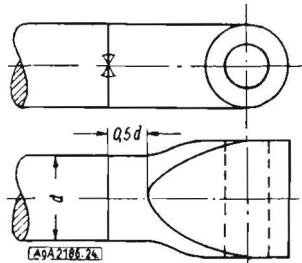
Ähnliche Ausführung wie in Bild 23, doch ist hier das Gelenkauge aus dem Vollen gefertigt. Ebenfalls gut für die Stumpfschweißung (Abbremschweißung) geeignet. Doch eignet sie sich nicht für hohe spezifische Gelenkdrücke
